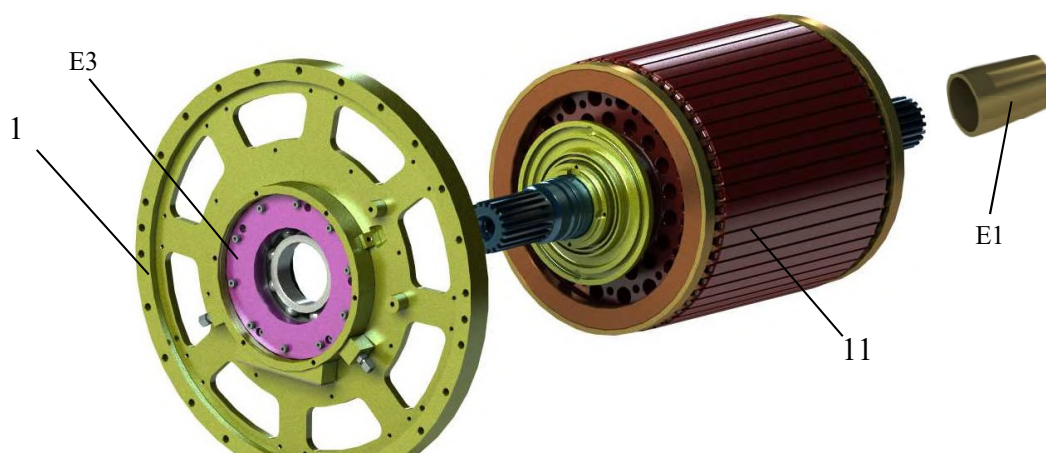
Монтаж щита подшипникового со стороны привода на ротор
